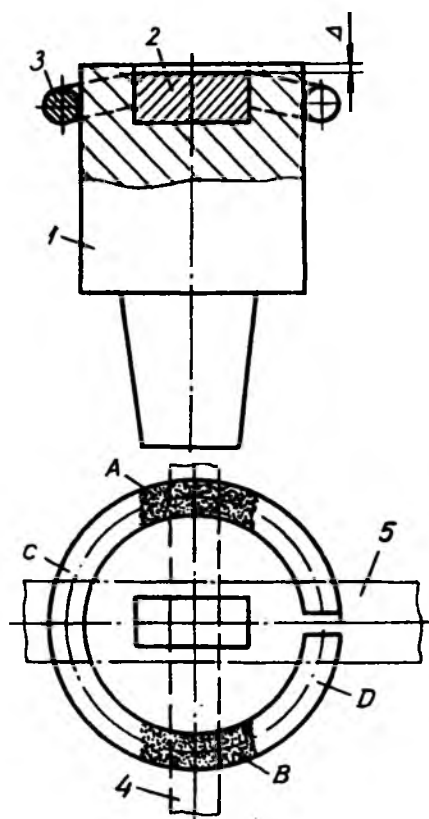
Электрод для контактной сварки арматурной проволоки
